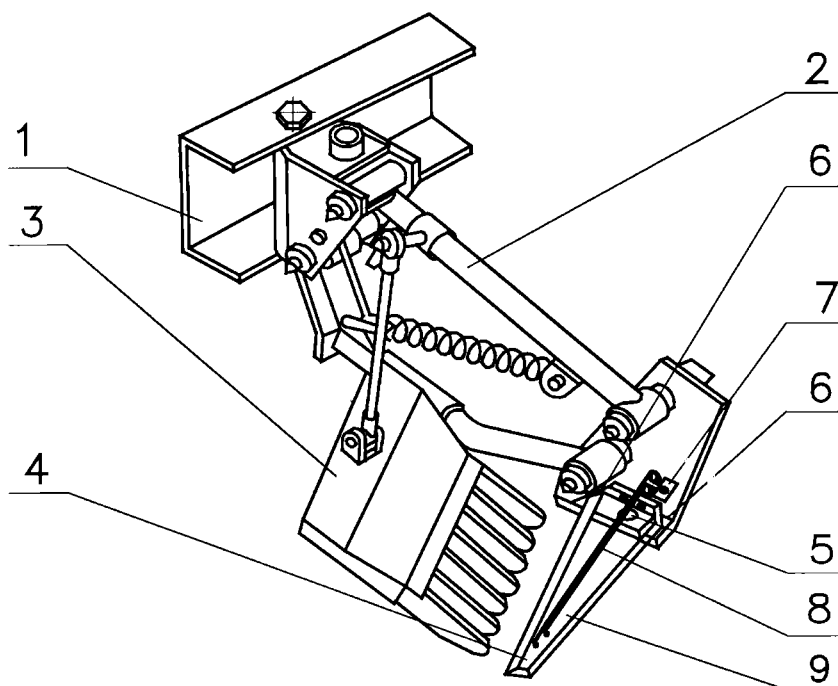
Конструктивна схема гичкозрізувального пристрою з підпружиненим ножем: 1 – рама; 2 – паралелограмна підвіска; 3 – гребінчастий копір; 4 – ніж; 5 – вісь обертання; 6 – упори; 7 – пластинка; 8 – пружина; 9 – ніж
